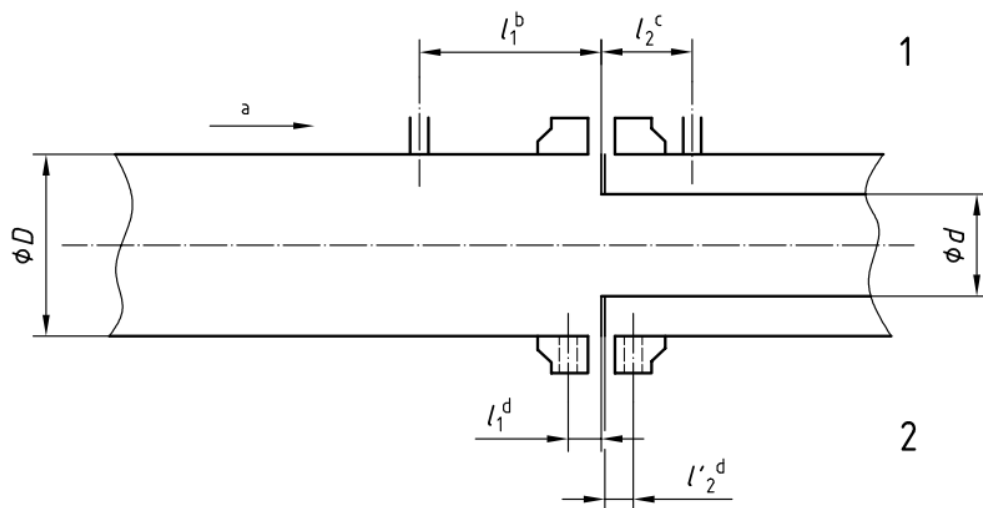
tubería genérica con tomas tipo brida (Flange) y D y D/2, corte longitudinal.
